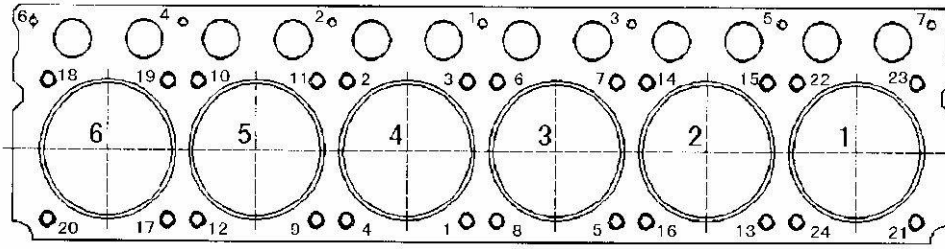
Последовательность затяжения главного болта и вспомогательной гайки головки цилиндра
